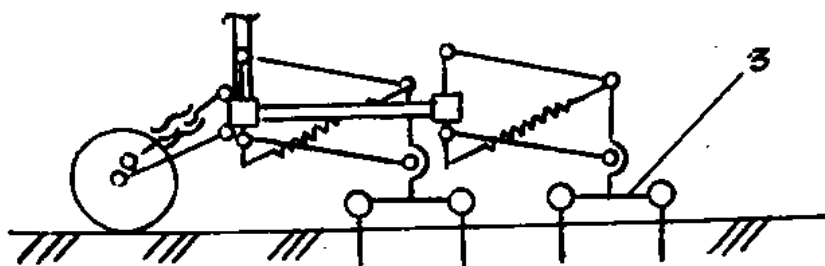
Схема орудия для поверхностной обработки почвы: 1 - рама; 2-параллелограммный механизм; 3 - рыхлитель; 4 - опорное колесо
